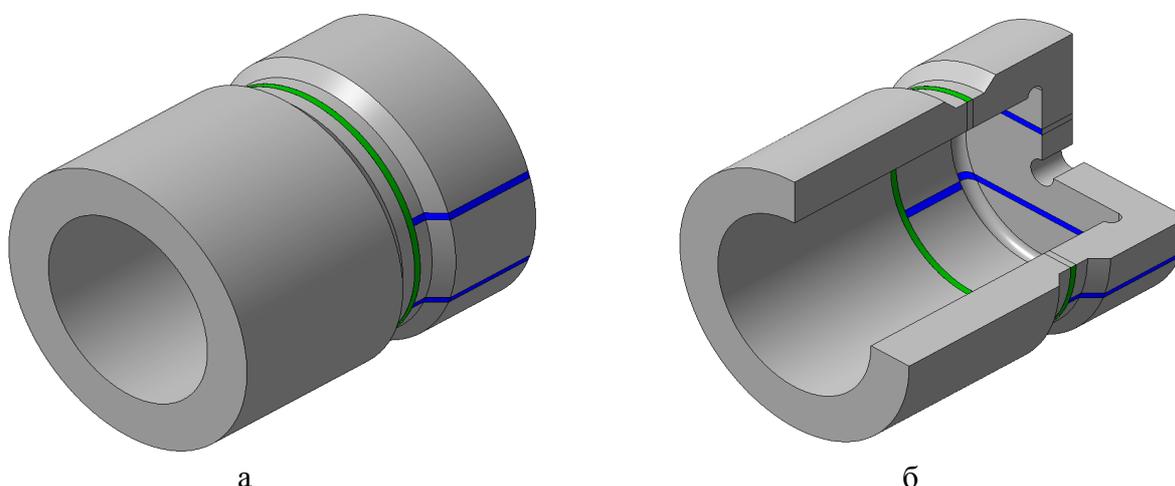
Общий вид сваренного цилиндра (а) и его разрез (б)
